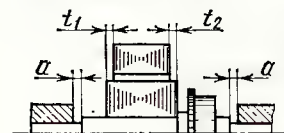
Осовой разбег ротора в подшипниках скольжения
